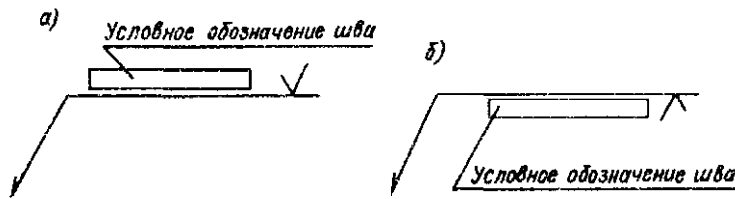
Нанесение обозначения шероховатости обработанной поверхности сварного шва: а — шов на лицевой стороне; б — шов на оборотной стороне
